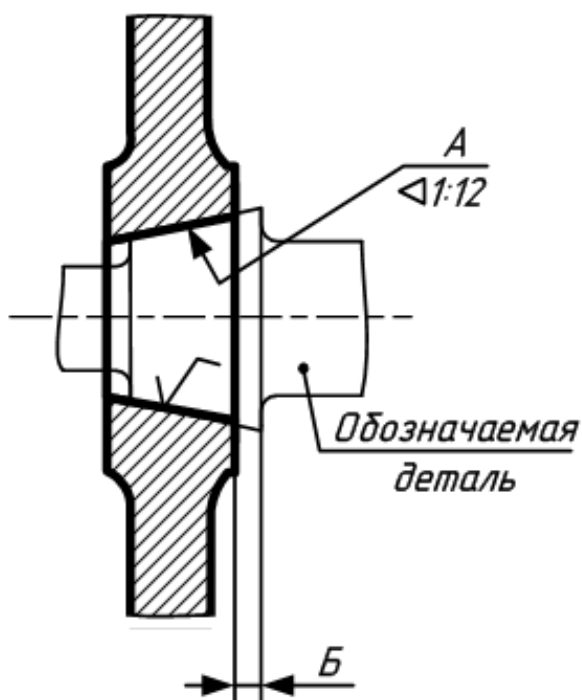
Обозначение размеров с предельными отклонениями элементов, обрабатываемых совместно с корпусом
